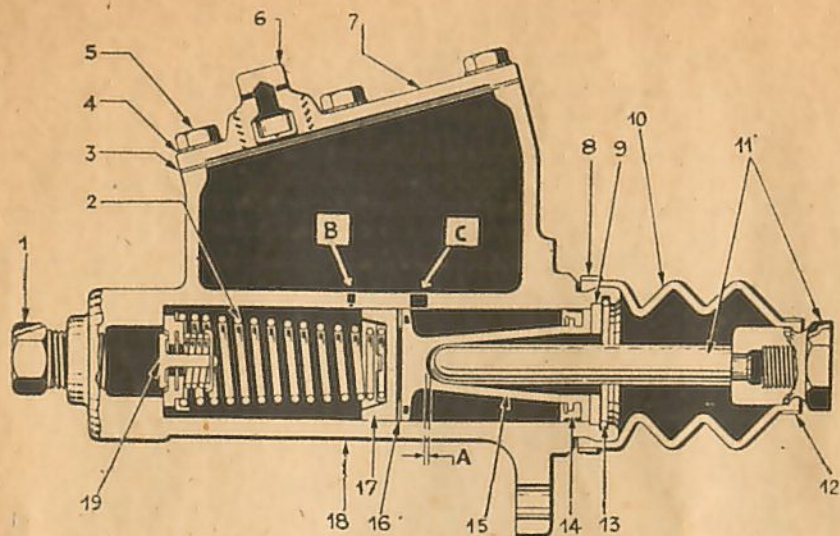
Vue en coupe du maître-cylindre Lockheed.
